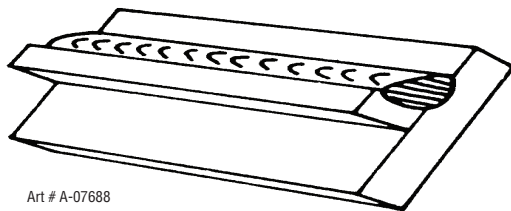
Soudure à plat, d'angle par gravité
